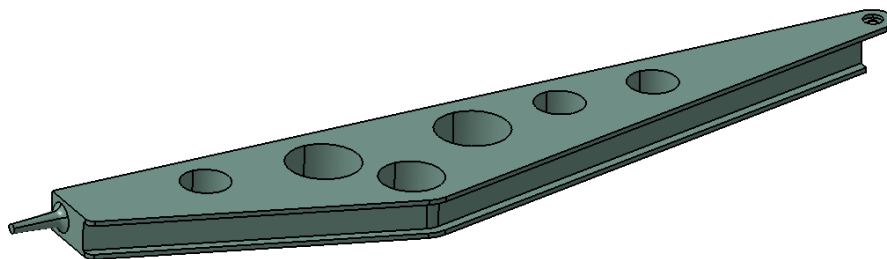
Seat mounting frame 11*: Parte principal modelada en CATIA
